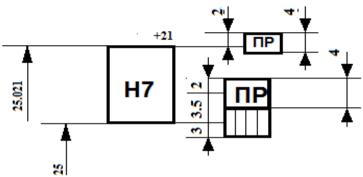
Схема расположения полей допусков рабочих калибров для отверстия Ø25H7(± 0.021)
